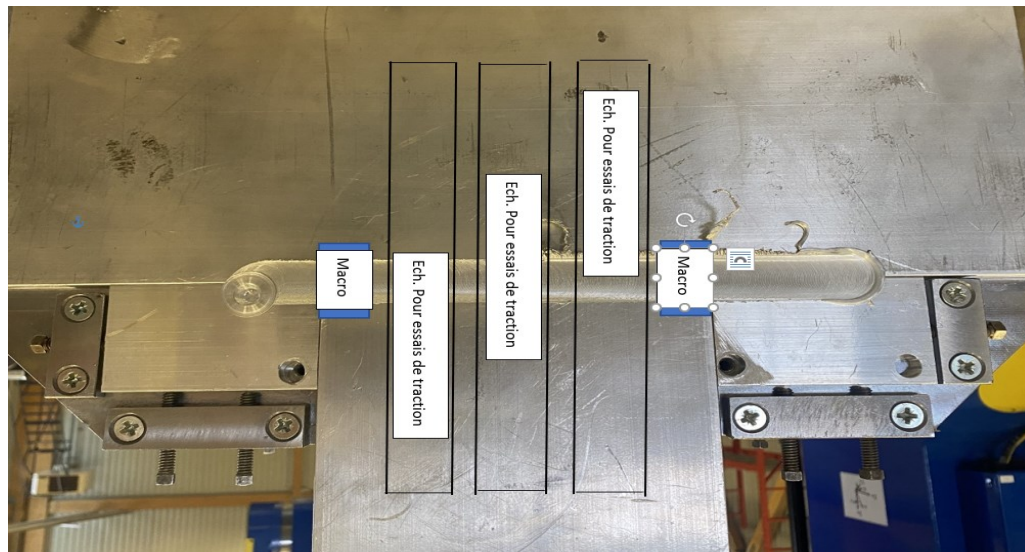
Prélèvement d'échantillons après soudure
